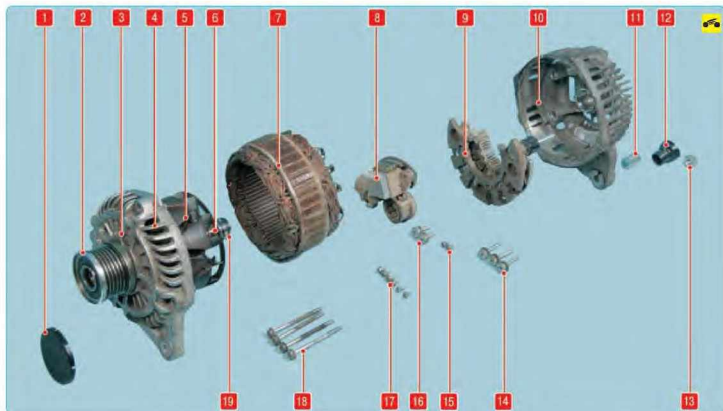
Детали генератора: 1 – крышка болта крепления шкива; 2 – шкив; 3 – винт крепления прижимной пластины переднего подшипника; 4 – передняя крышка; 5 – ротор; 6 – контактные кольца; 7 – статор; 8 – щеткодержатель с регулятором напряжения; 9 – выпрямительный блок; 10 – задняя крышка; 11 – дистанционная втулка; 12 – изоляционная втулка контактного болта; 13 – гайка контактного болта; 14 – винты крепления выпрямительного блока; 15, 16 – винты крепления щеткодержателя; 17 – винты крепления выводов обмотки статора; 18 – стяжные болты; 19 – задний подшипник ротора
